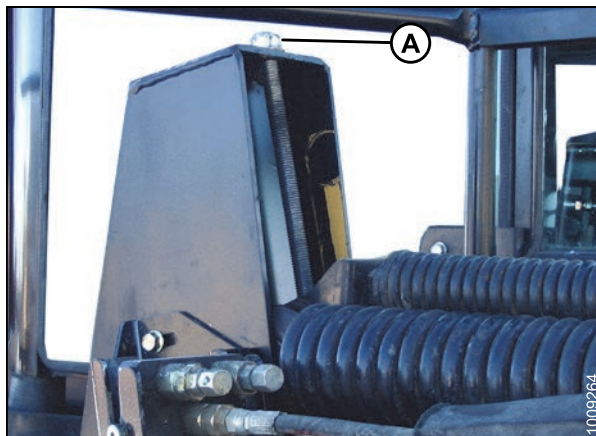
Регулировочный болт — показан верх опорной стойки колеса валковой косилки
